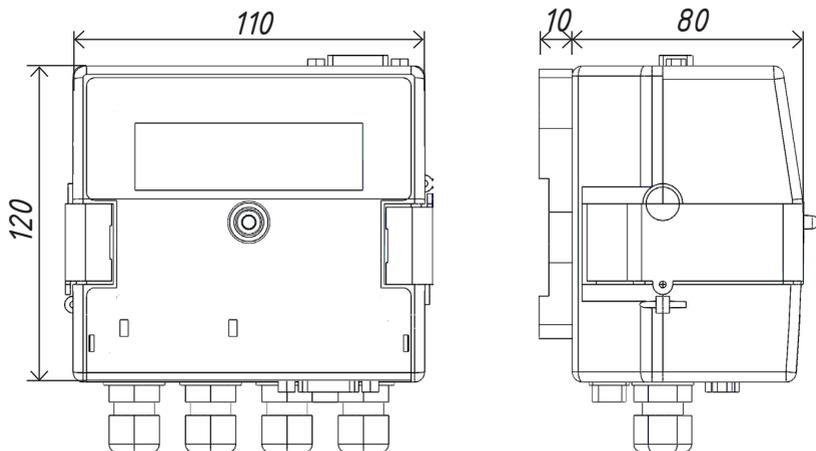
ж - Габаритные размеры электронного блока с накладкой для крепления на DIN – рейку
